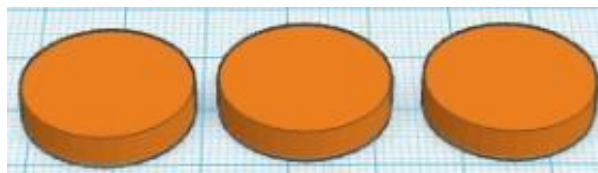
TROIS OBJETS CYLINDRES SUR LE PLAN DE TRAVAIL
